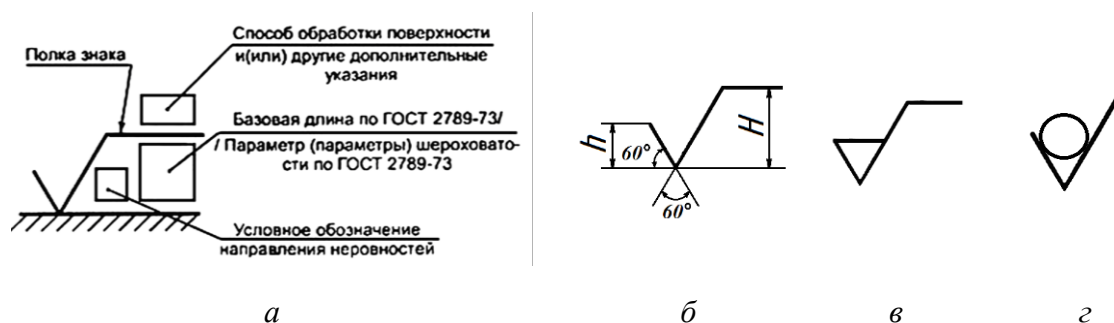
Обозначение шероховатости: *а* – структура; *б* – геометрические соотношения знака шероховатости; *в* – знак, используемый для обозначения шероховатости поверхности, образуемой со снятием слоя материала; *г* – знак, используемый для обозначения шероховатости поверхности, образуемой без удаления слоя материала
